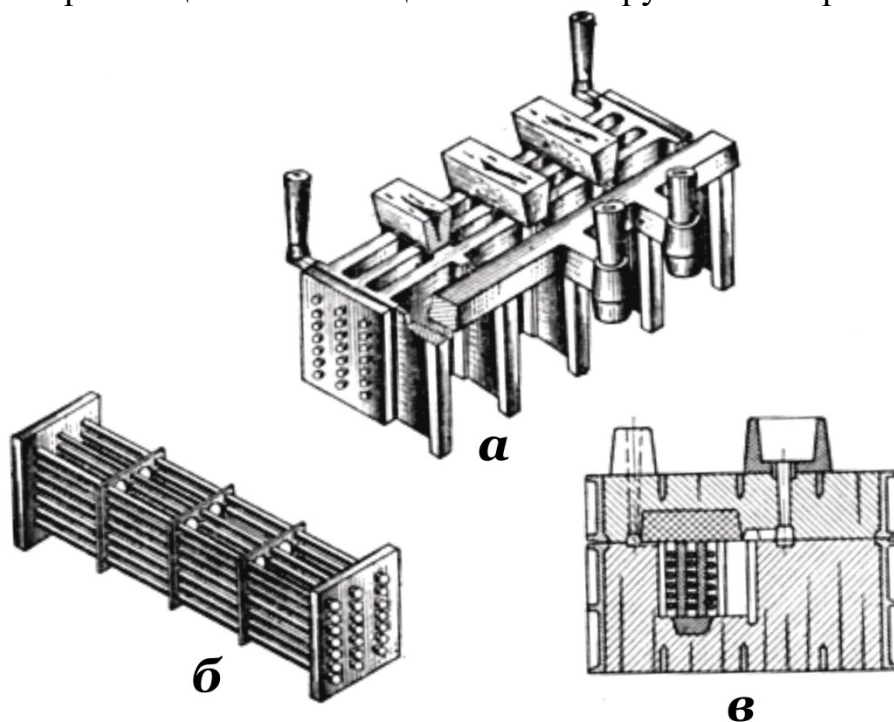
Изготовление армированной отливки рекуператора типа «термоблок»: а – отливка рекуператора с литниковой системой; б – стальной каркас, заливаемый в отливке; в – разрез собранной формы
